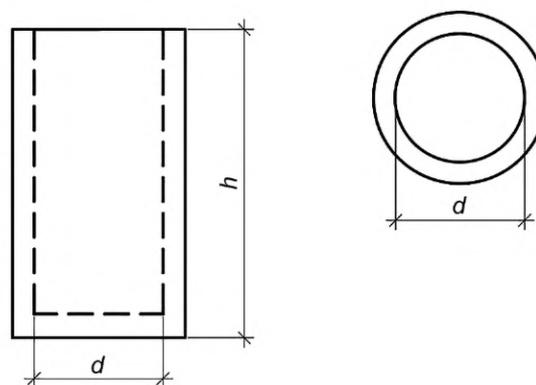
Формы для изготовления образцов в виде цилиндра. Тип ФЦ
